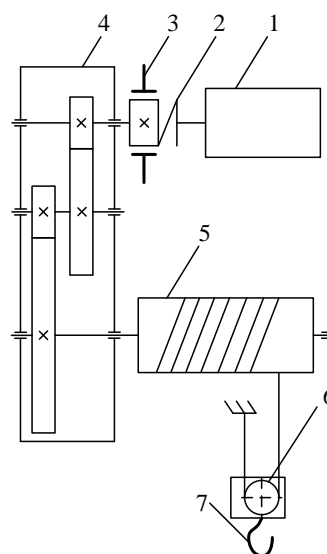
Кінематична схема підйомної лебідки: 1 – двигун; 2 – муфта; 3 – гальмо; 4 – механічна передача (редуктор); 5 – барабан; 6 – блок поліспастів; 6 – вантажозахватний пристрій
